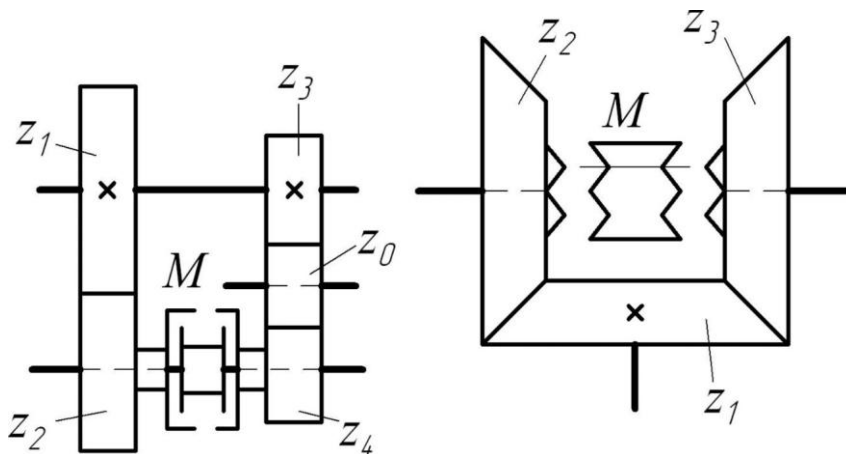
Реверсивні механізми металорізальних верстатів
